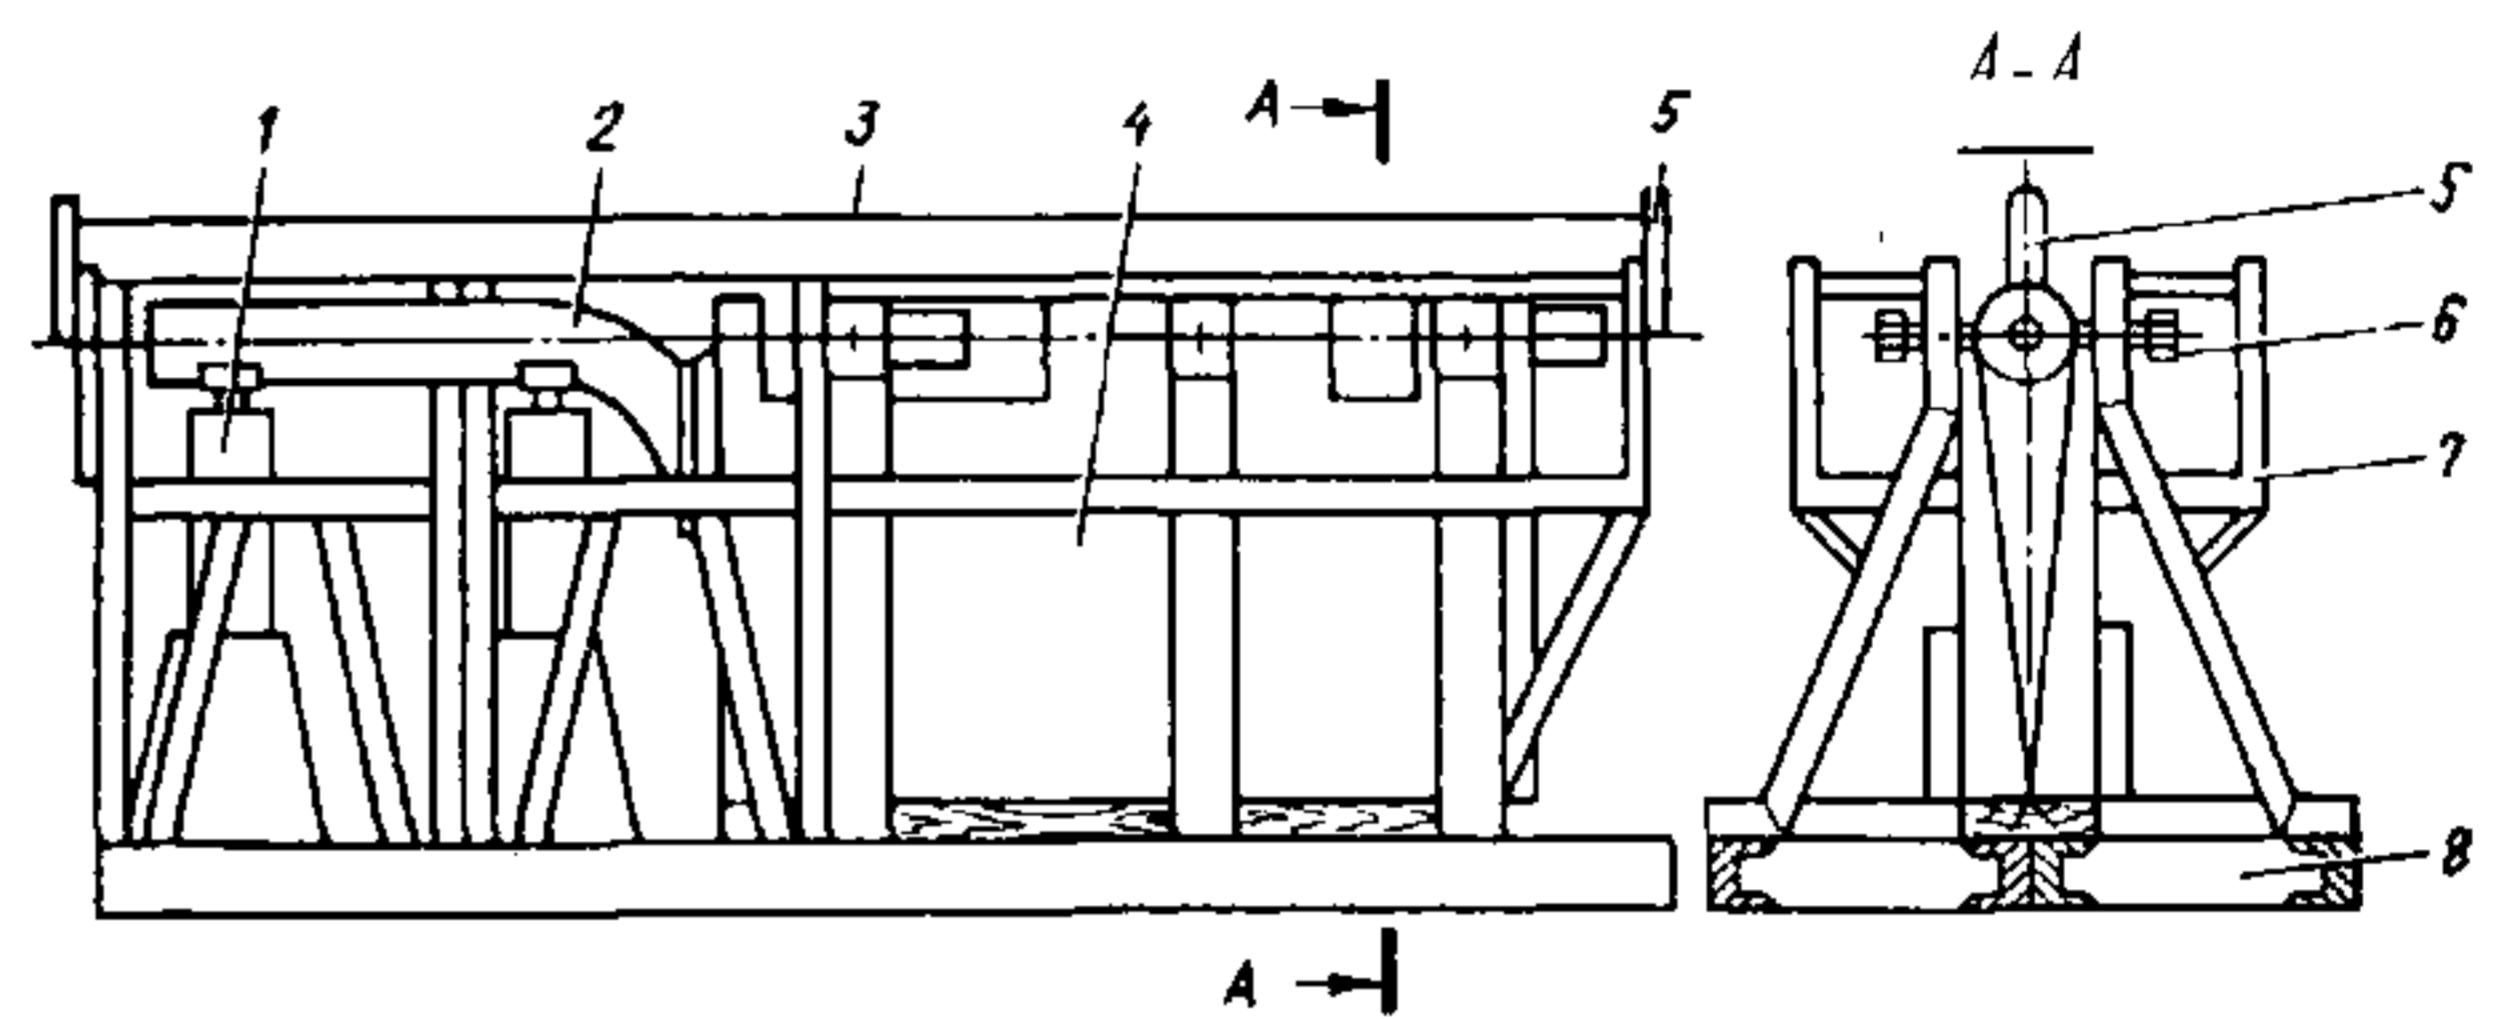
Универсальный стенд для проверки соосности баллера пера руля:
